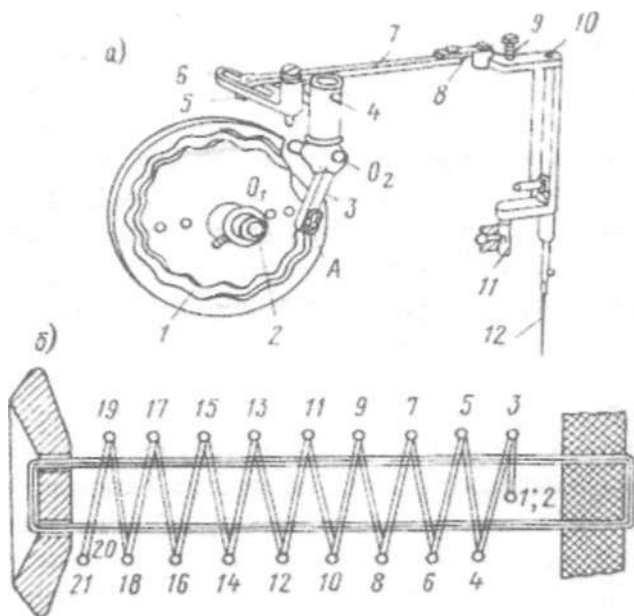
Полуавтомат для оббивки стойки пуговицы: а - схема механизма поперечных отклонений иглы; б - схема оббивки стойки пуговицы
